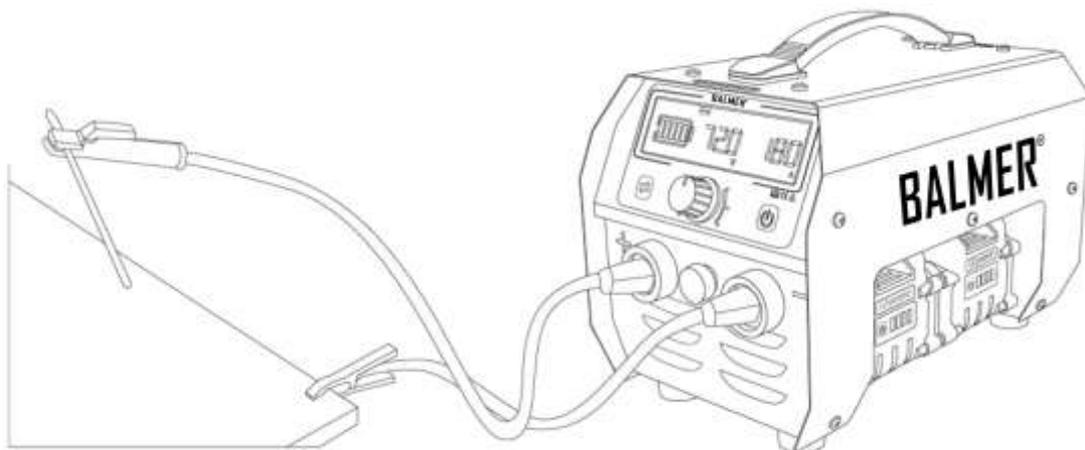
Indicação de conexão de soldagem com eletrodo revestido.
